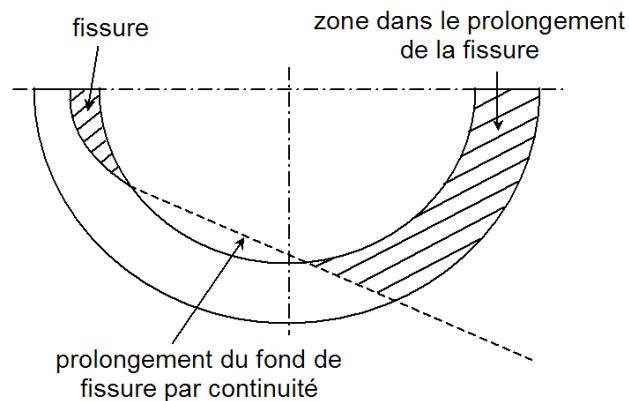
a : Coupe horizontale dans le plan de la fissure
